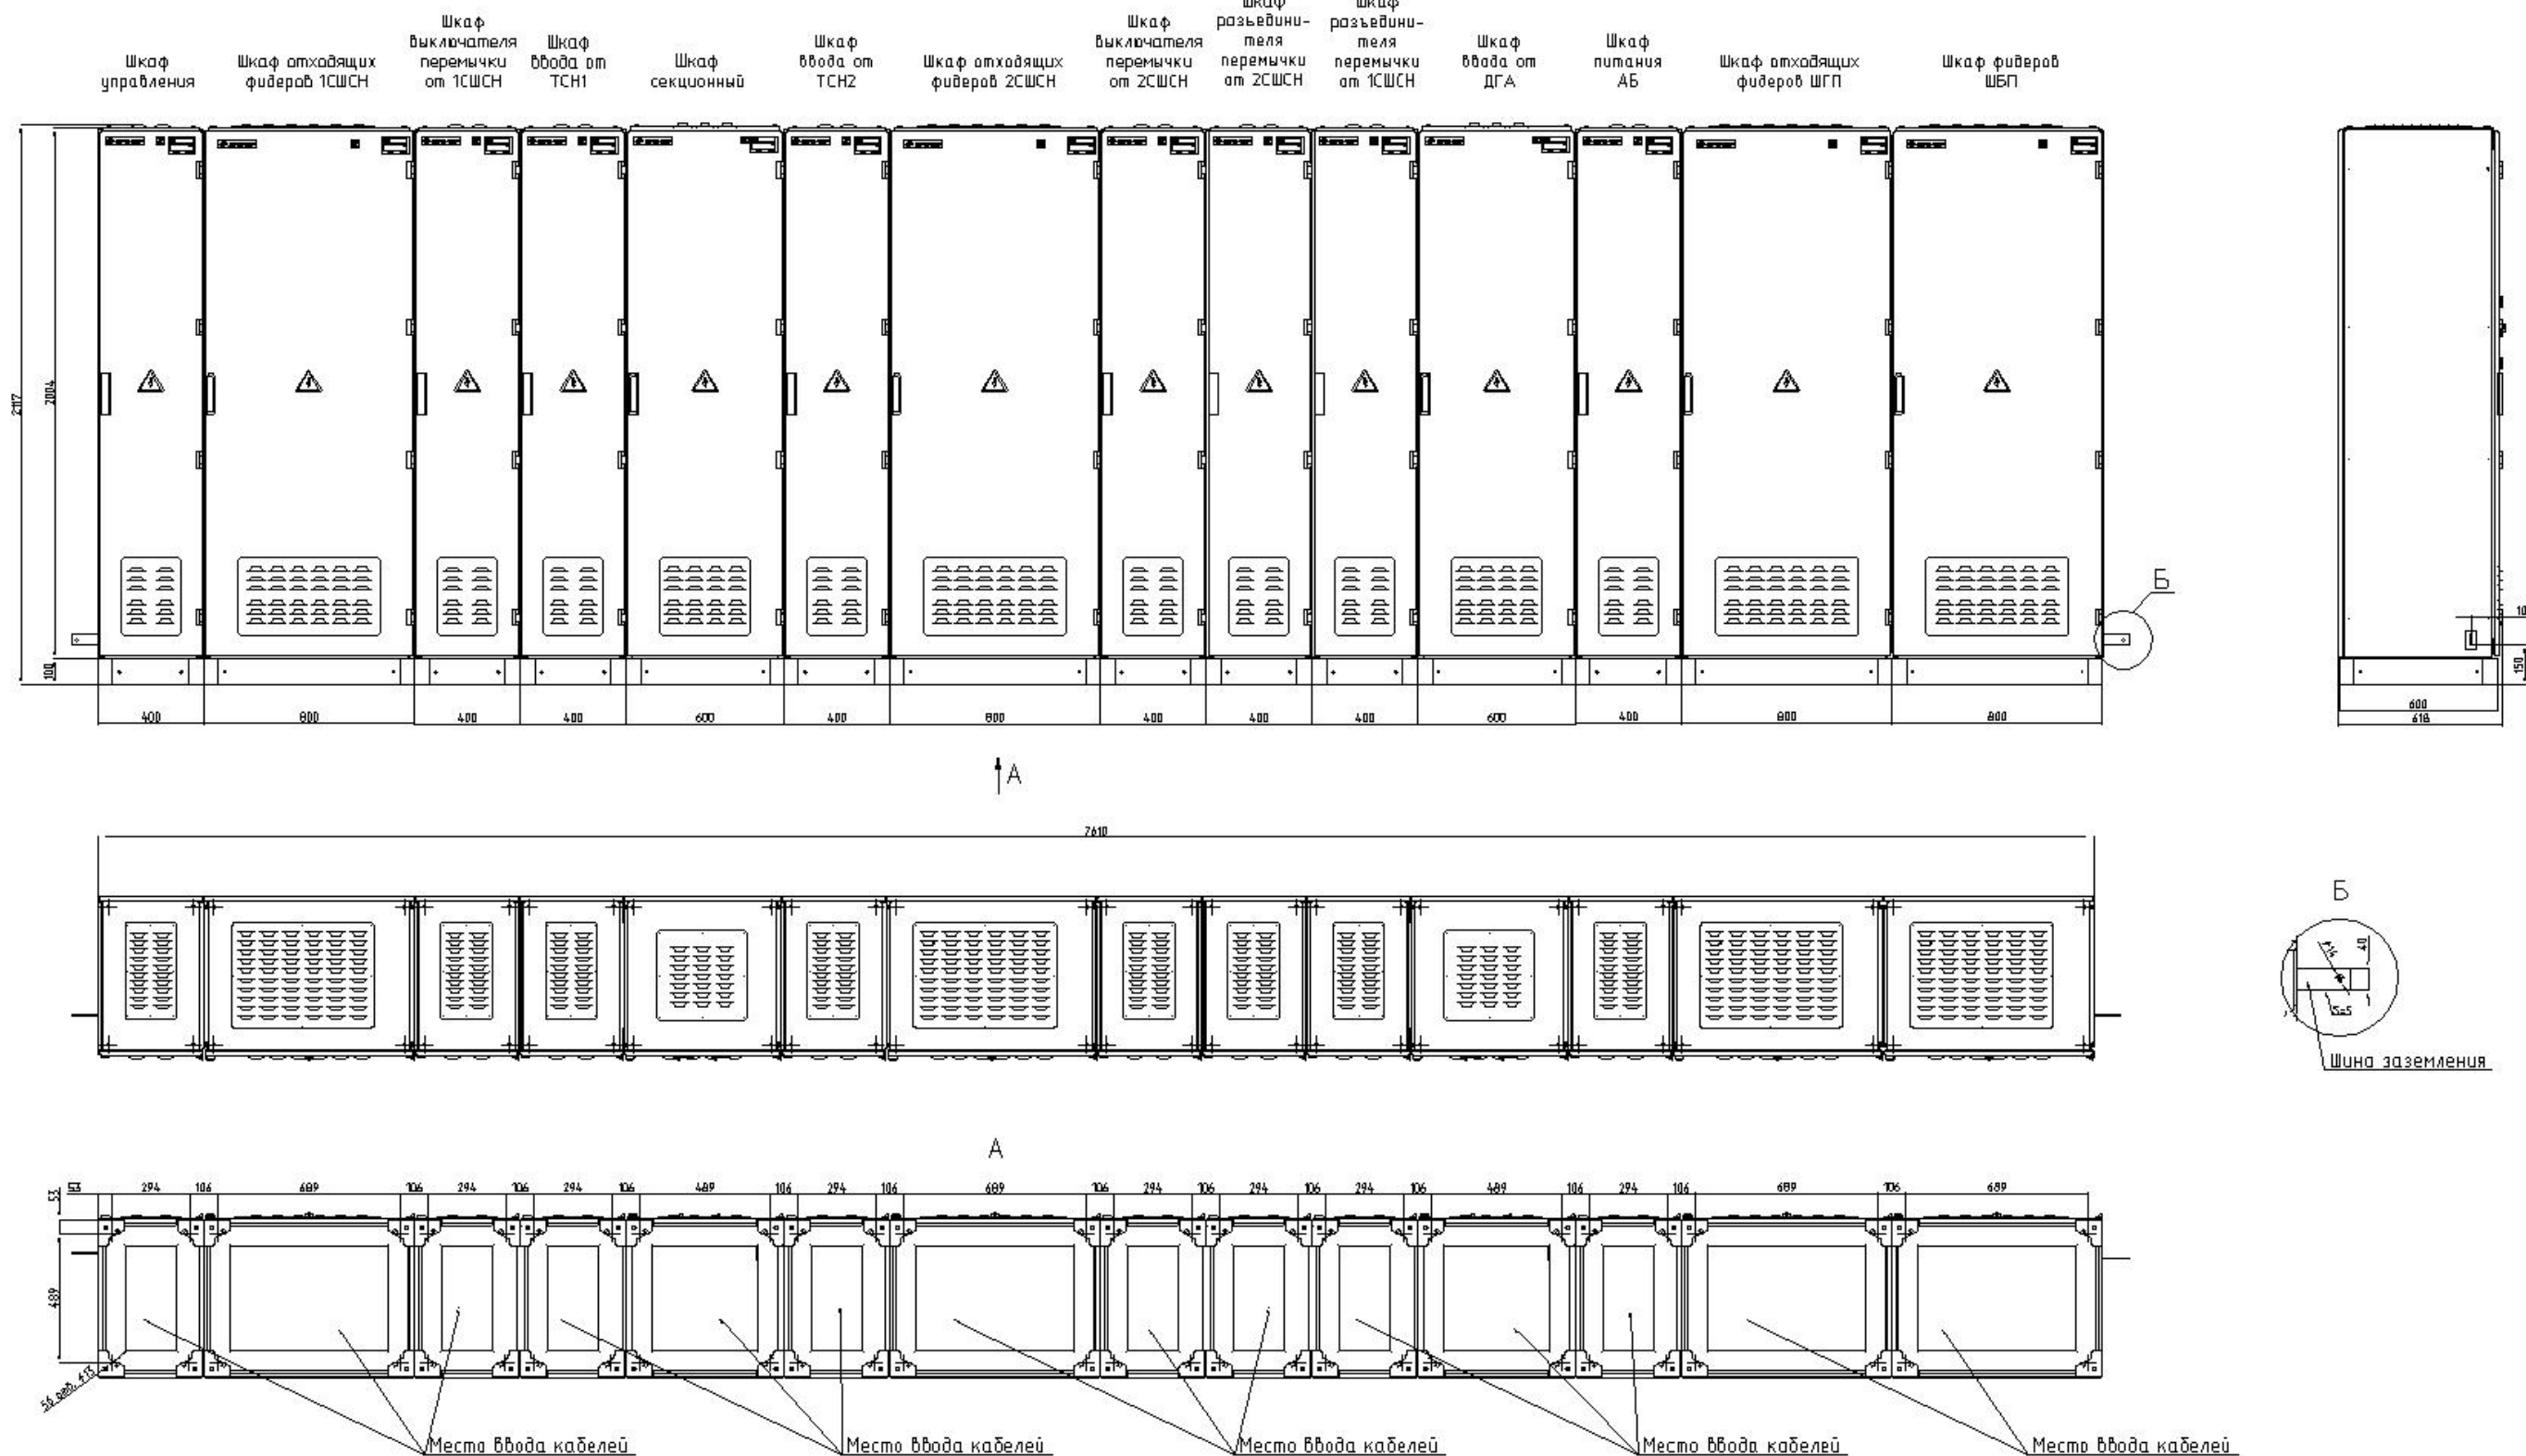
Габаритный чертеж блока СН переменного тока 630 А (с цоколем 100 мм)
